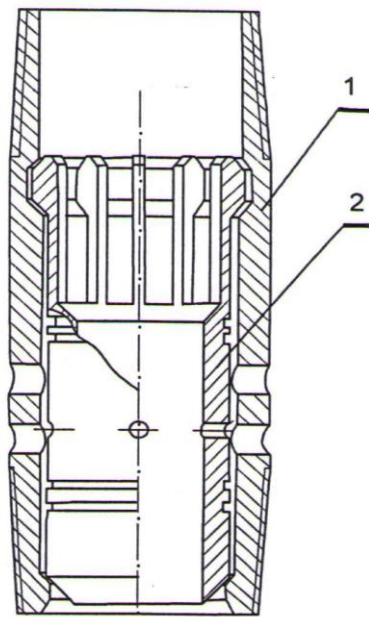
Перфорированный патрубок с забойным штуцером: 1 - перфорированный патрубок; 2 - забойный штуцер
